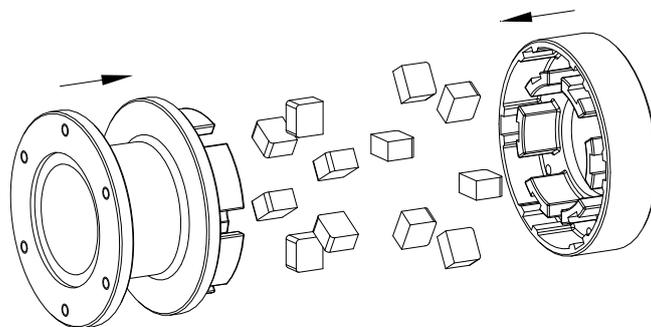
Montaggio di flange di trasmissione, elemento intermedio e pezzi in elastomero
